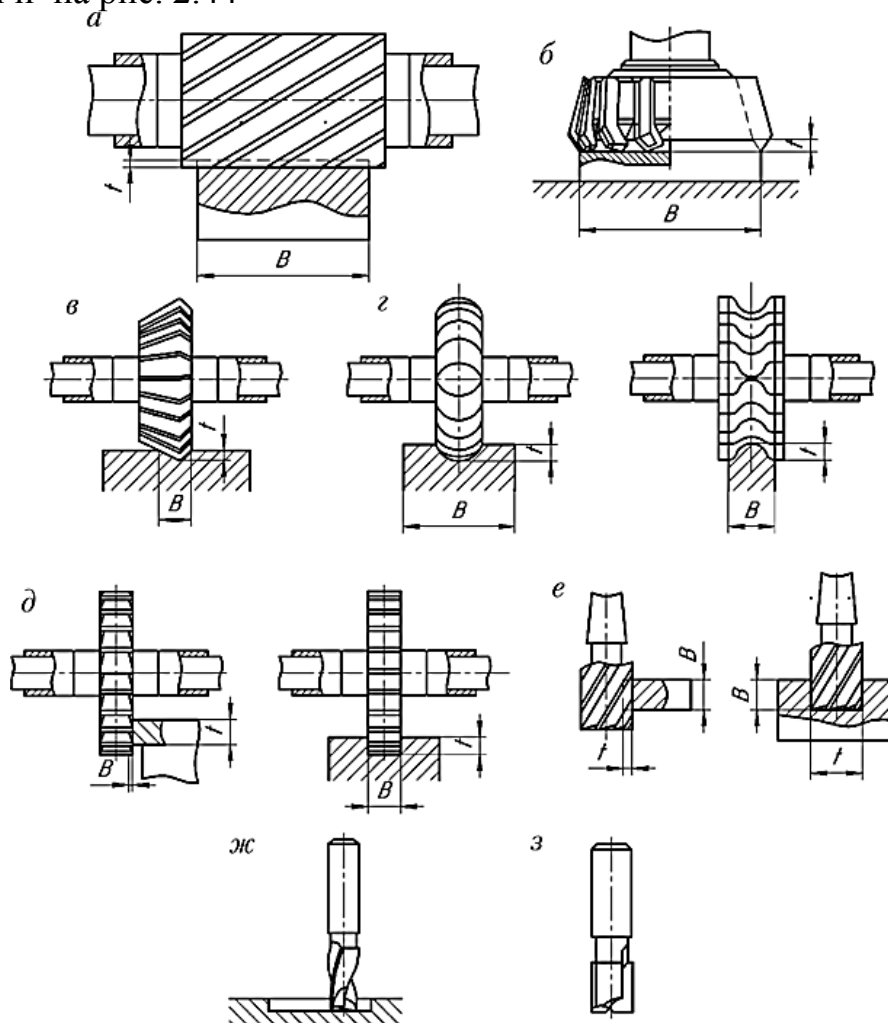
Типы фрез и обрабатываемых поверхностей
